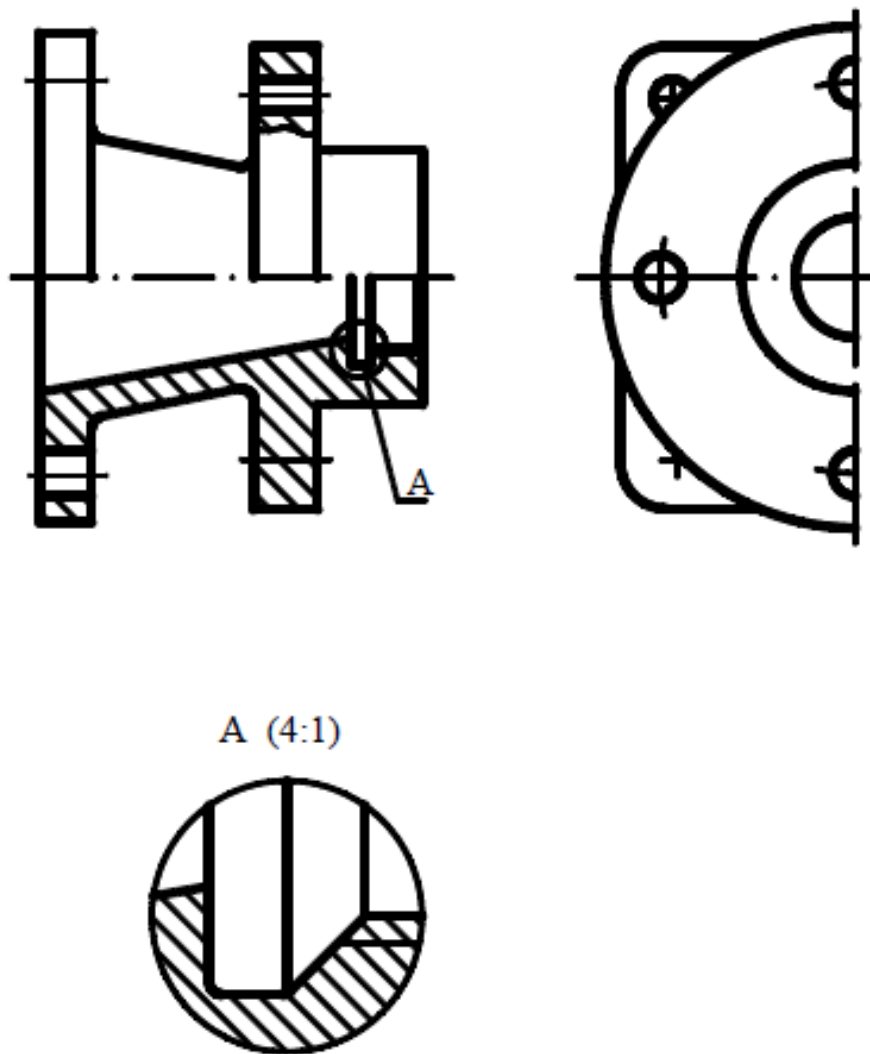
Третий этап выполнения рабочего чертежа детали по чертежу общего вида (детализирование)
